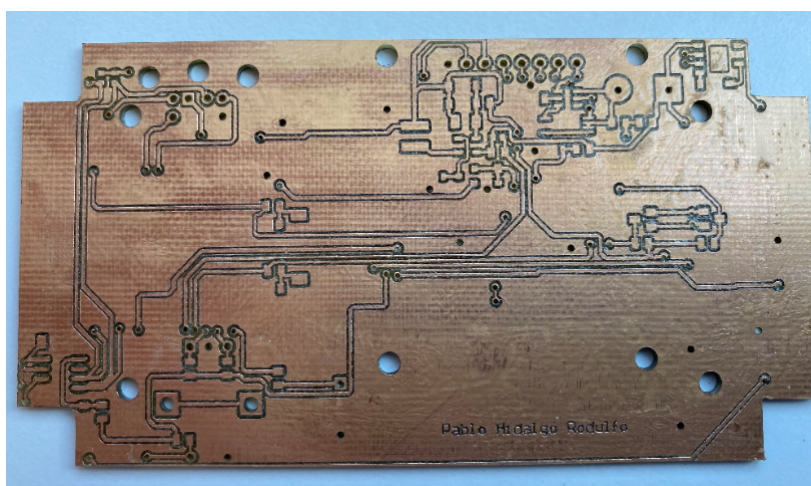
Vista inferior PCB fabricada en GranaSAT
